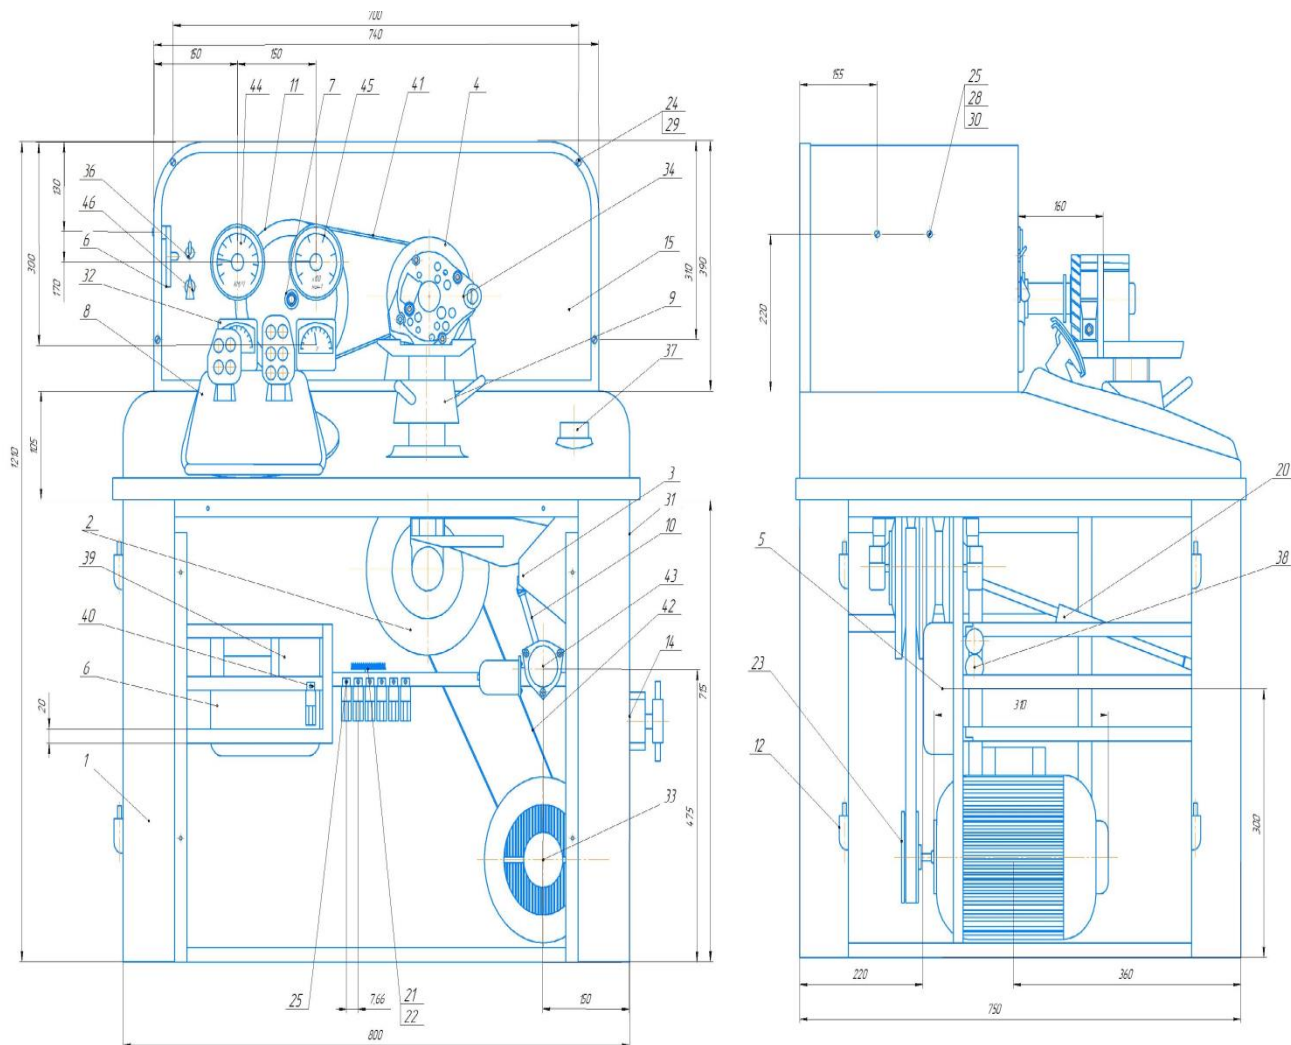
Общий вид «Стенд для автоматического управления бесступенчатой коробкой передач»
